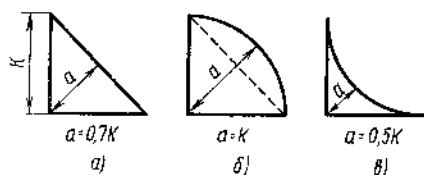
Основные конструктивные элементы наплавочных швов:
